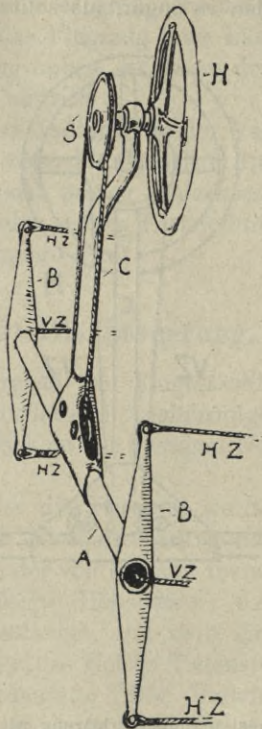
Handradsteuerung. *H* = Handrad; *A* = Höhensteuerachse; *B* = Schwinghebel; *C* = Steuersäule; *S* = Seilscheibe; *VZ* = Quersteuerzüge; *HZ* = Höhensteuerzüge; *R* = Seilrollen.
